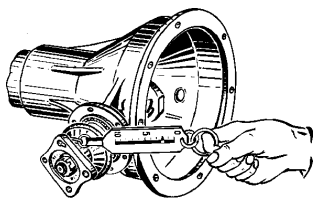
Проверка затяжки подшипников ведущей шестерни
